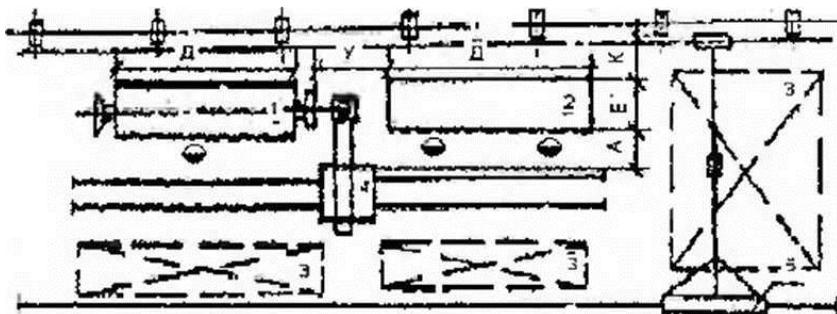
Размещение стенов, кантователей для сварки крупногабаритных узлов: 1 - двухстоечный кантователь; 2 - стенд для сборки; 3 - место складирования; 4 - универсальная площадка для сварщика с подвижной стрелой; 5 - полукозловой кран
